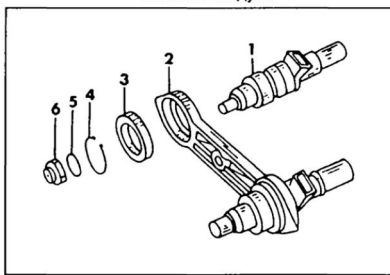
Форсунка и держатель. 1 - форсунка, 2 - держатель, 3 - кольцо резиновое, 4 - установочное кольцо, 5 - уплотнительное кольцо, 6 - изолирующий колпачок.
